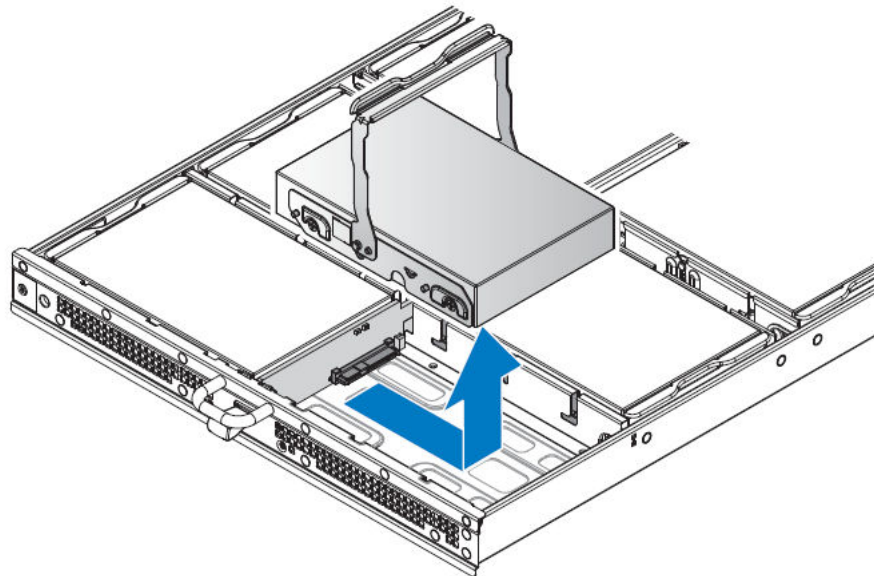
Entfernen der 3,5-Zoll-Festplattenbaugruppe
